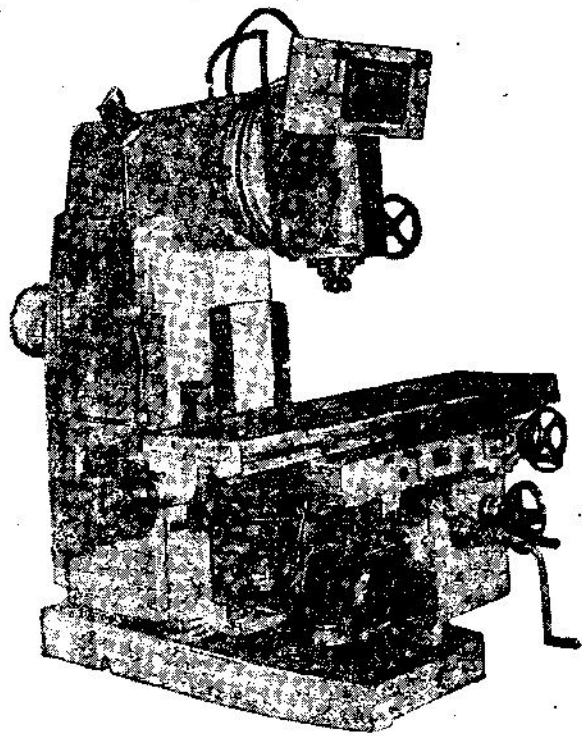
Станок фрезерный консольный моделей 6P13 и 6P13Б
